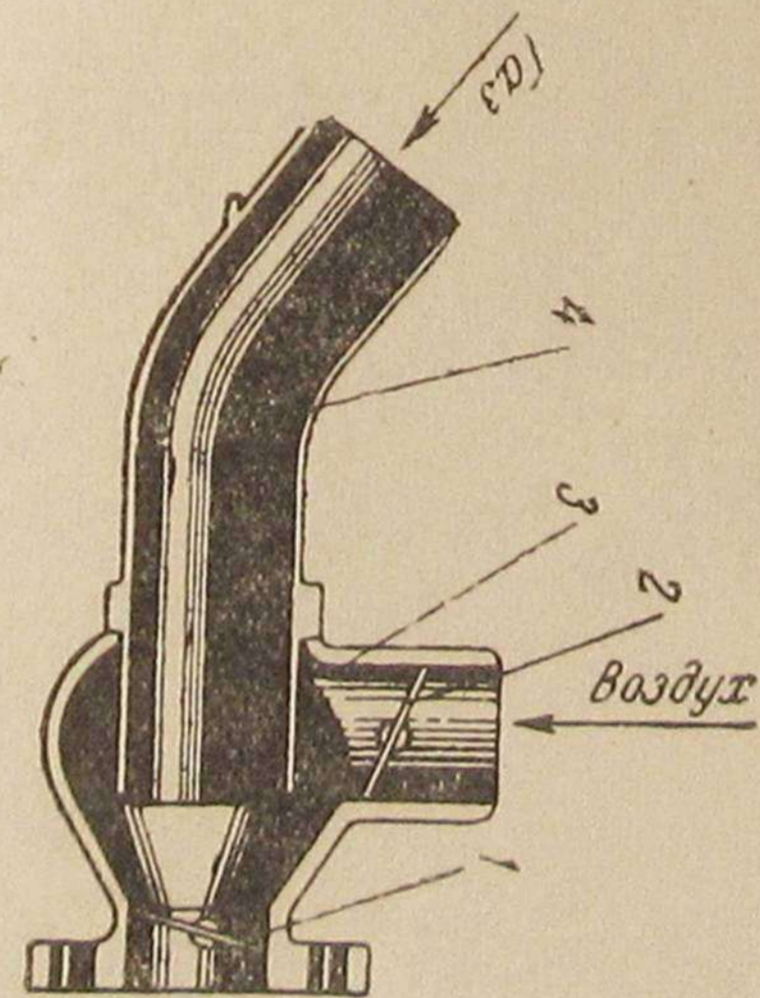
Смеситель ГАЗ—42: 1—дрессельная заслонка рабочей смеси (количественная регулировка), 2—дрессельная заслонка воздуха смесителя, 3—воздушный патрубок смесителя, 4—газовый патрубок смесителя.
